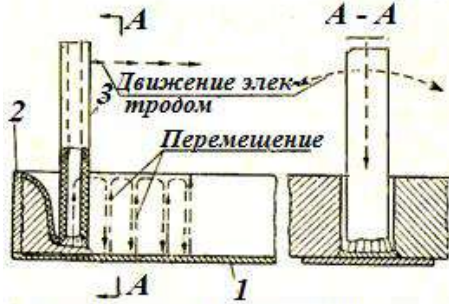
Схема сварки погруженной дугой
